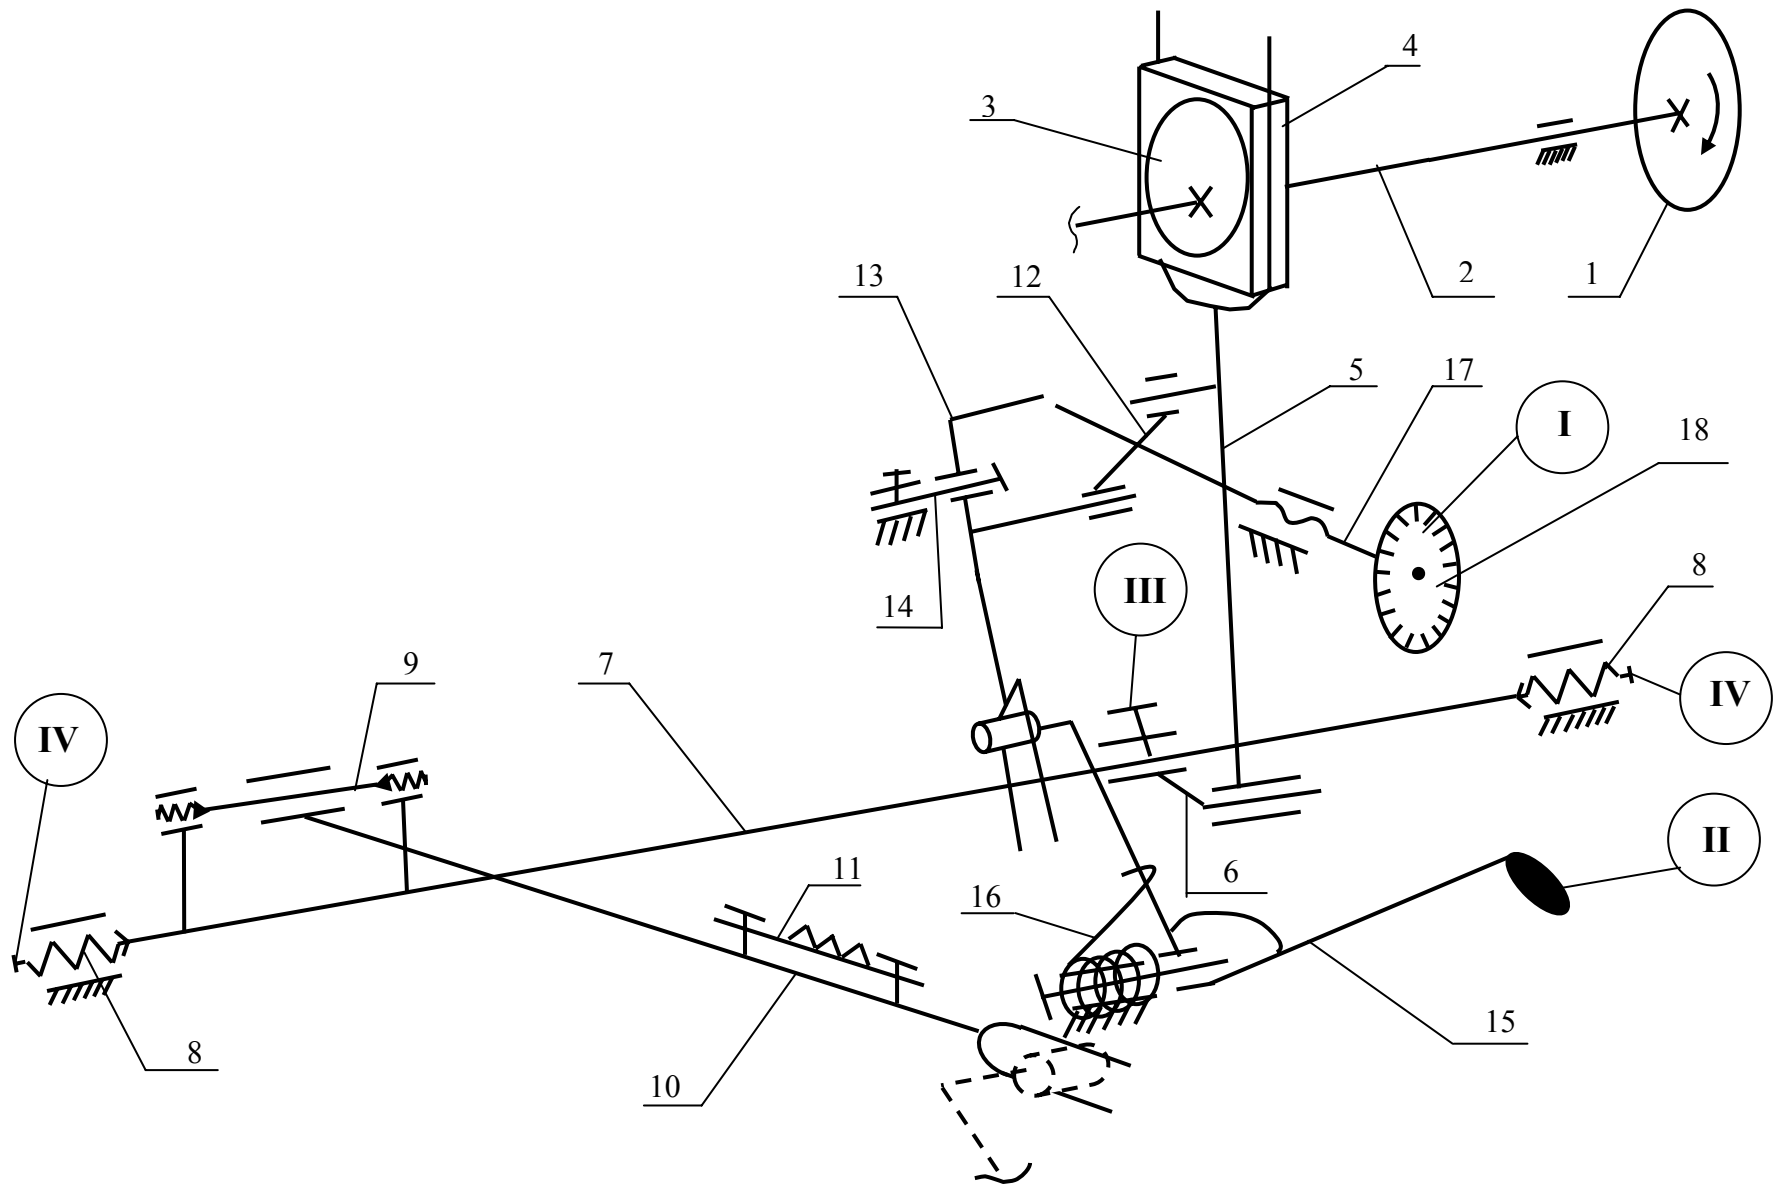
Кинематическая цепь подачи механизма перемещения материала
